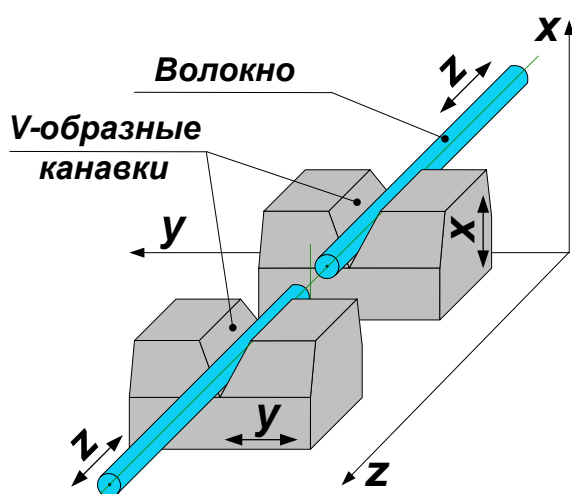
Юстировка волокон в сварочном аппарате
